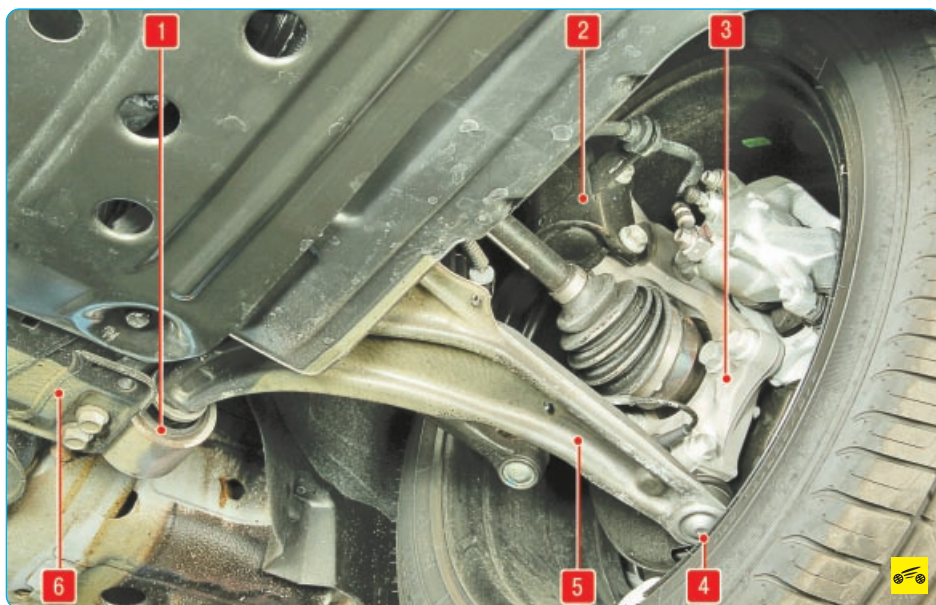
Передняя подвеска (левая сторона): 1 – кронштейн рычага подвески; 2 – амортизаторная стойка; 3 – поворотный кулак; 4 – шаровая опора; 5 – рычаг передней подвески; 6 – подрамник передней подвески
